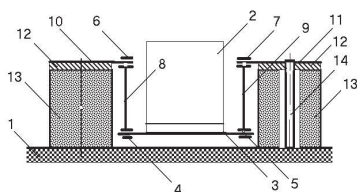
Конструктивная схема резинового виброизолятора с шарнирно - рычажным механизмом.
